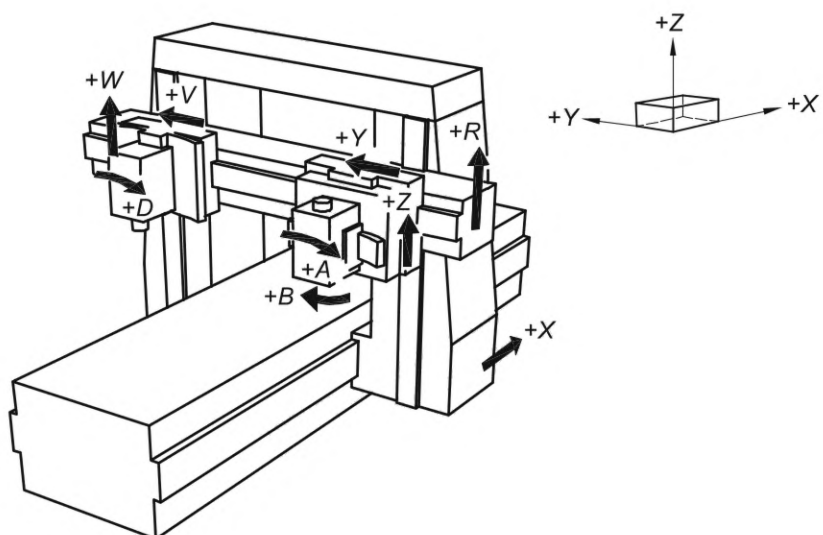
Продольно-фрезерный станок с подвижным порталом
